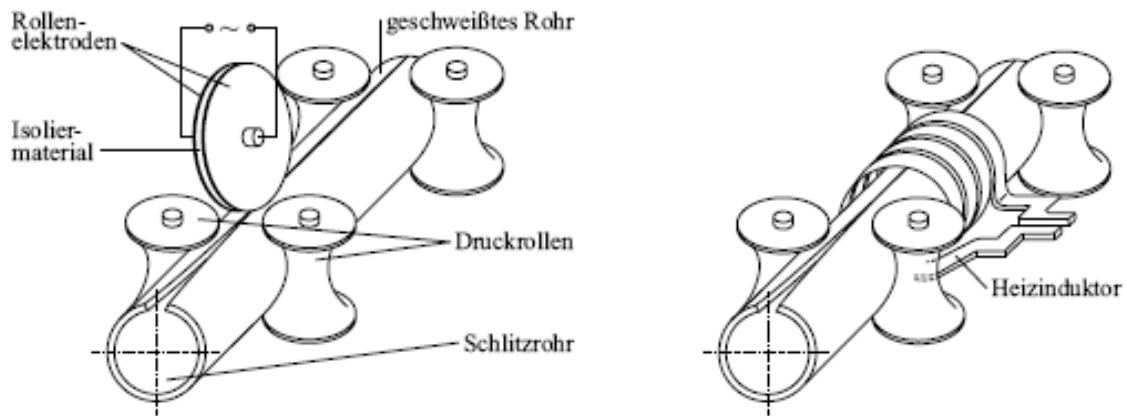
Widerstandsschweißen und HF-Schweißen von Rohren [13]
